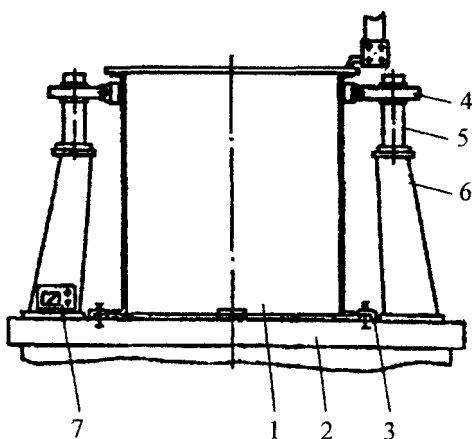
Схема крепления жесткой оболочковой конструкции на планшайбе карусельного станка:
